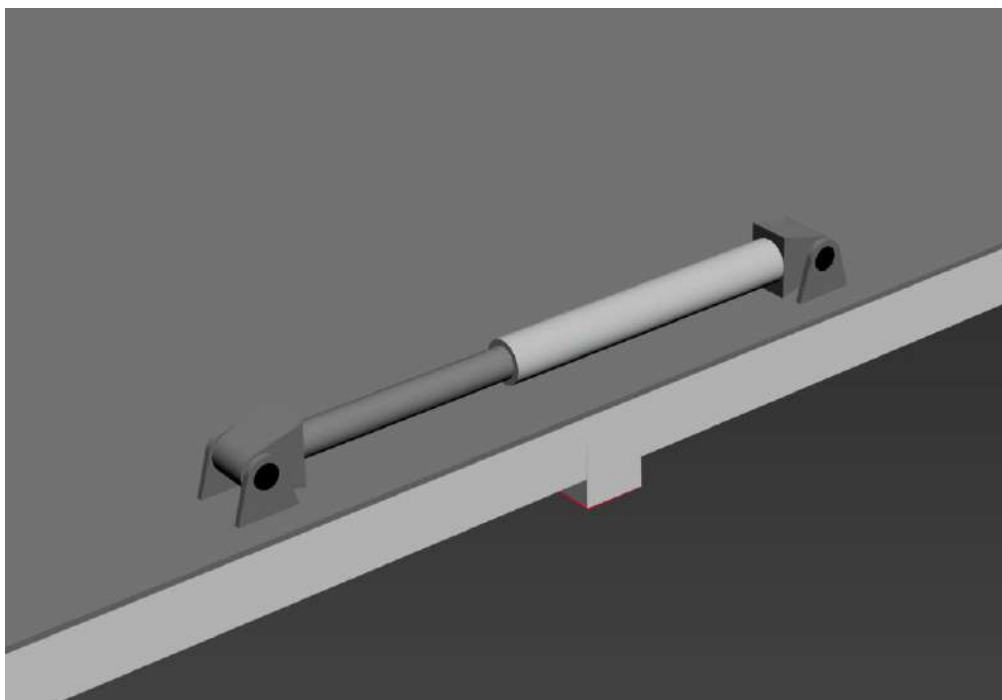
Render detalle sistema hidráulico container “Fuente: Elaboración propia”
